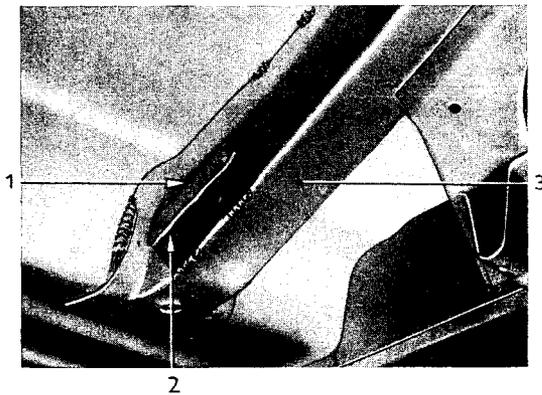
Innere Hinterfederstütze vom Flansch abgebrochen
